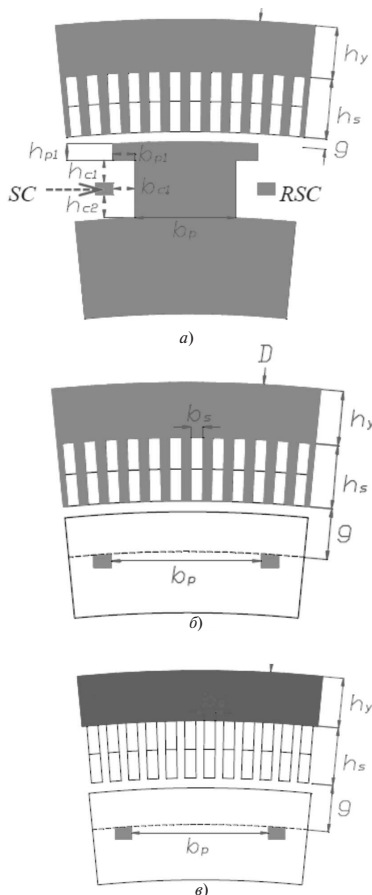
Топология ветрогенераторов со сверхпроводниковой обмоткой возбуждения: а – ферромагнитный статор–ферромагнитный ротор; б – ферромагнитный статор–неферромагнитный ротор; в – неферромагнитный статор–неферромагнитный ротор
